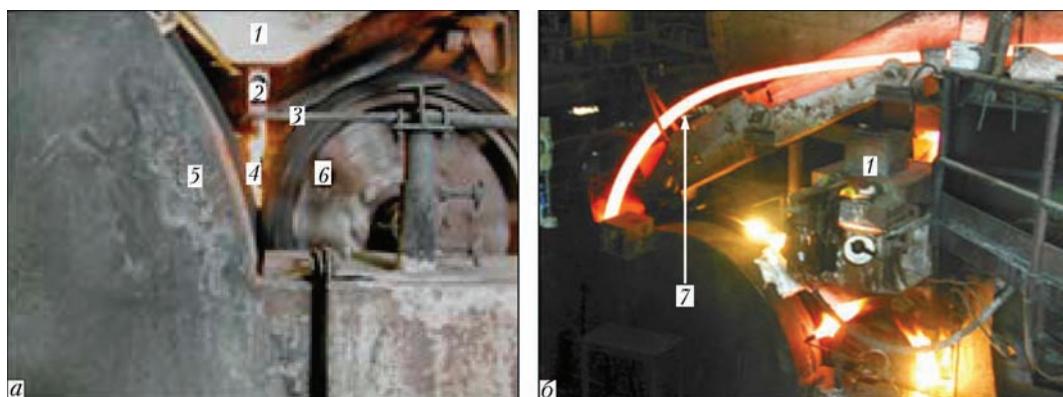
Процесс подачи расплава в кристаллизатор (а) и выхода заготовки с колеса (б) на роторной МНЛЗ: 1 — промежуточный ковш; 2 — керамический стакан; 3 — газовая горелка для подогрева расплава; 4 — струя расплава; 5 — рабочее колесо в защитном кожухе; 6 — прижимной ролик; 7 — непрерывнолитая заготовка
